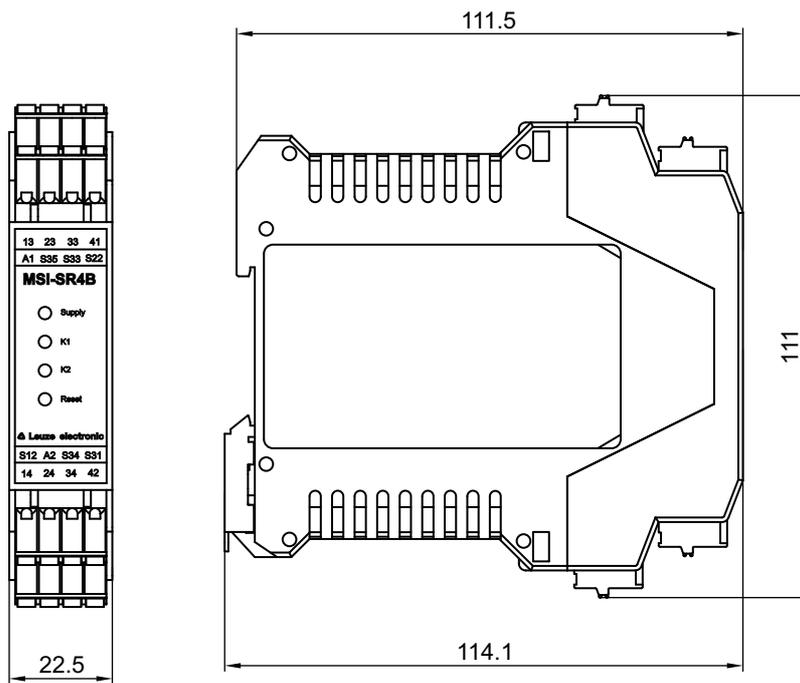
Dimensioni dell'MSI-SR4B-02
